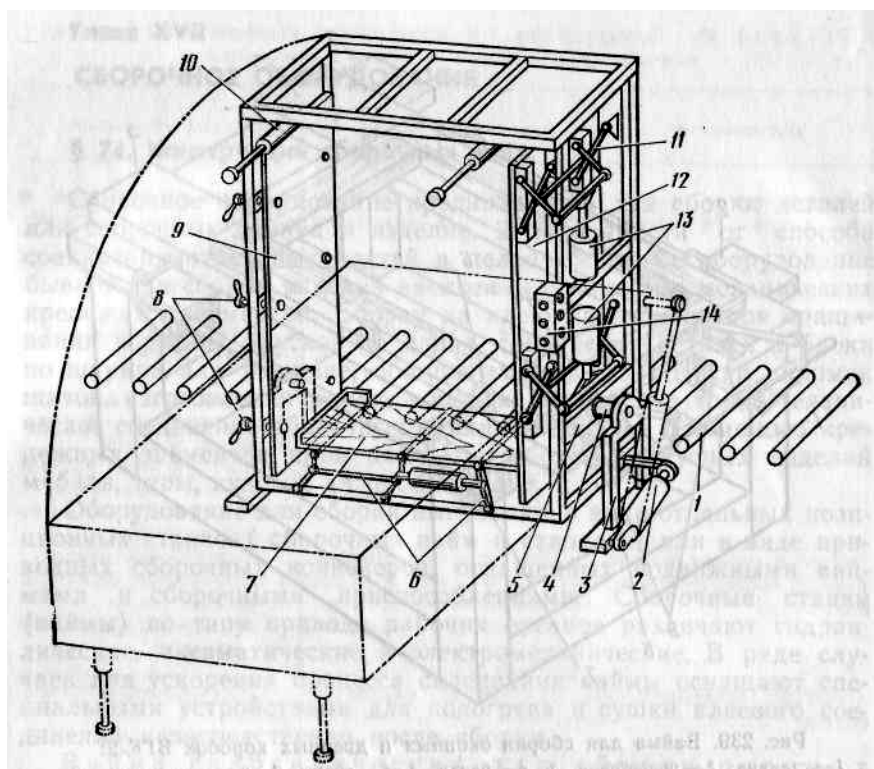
Пневматическая вайма для сборки корпусной мебели:
